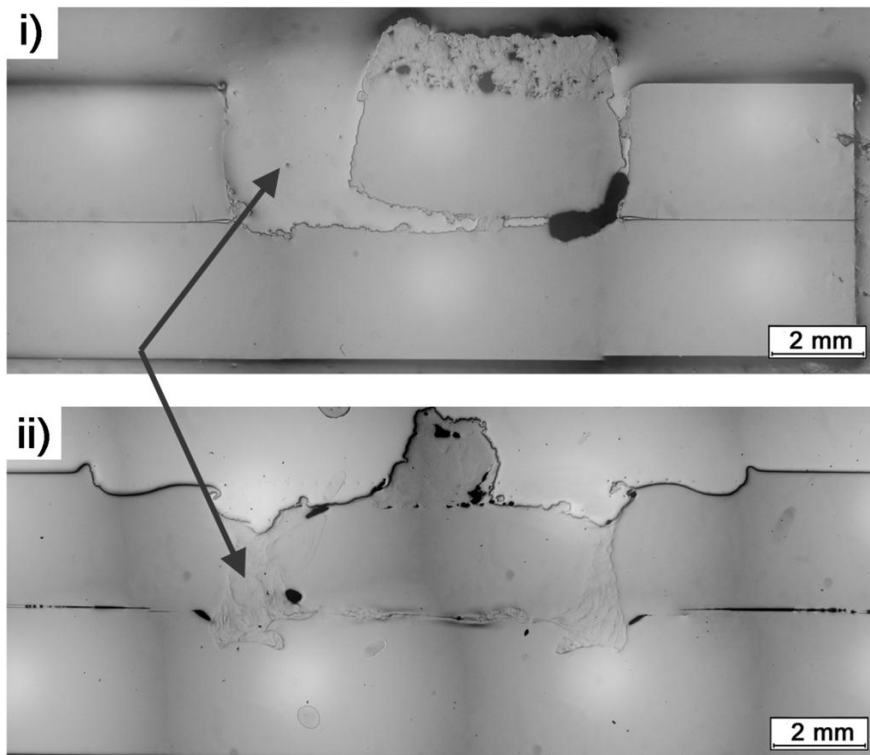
Seção transversal das amostras de PMMA soldadas por FSpW. i) Amostra soldada com a ferramenta de aço inoxidável (500 RPM/ 3+4 s/ 4 mm). ii) Amostra soldada com a ferramenta de liga de titânio (500 RPM/ 1,5+4 s/ 4 mm). Em destaque, as regiões de preenchimento do furo da solda.
